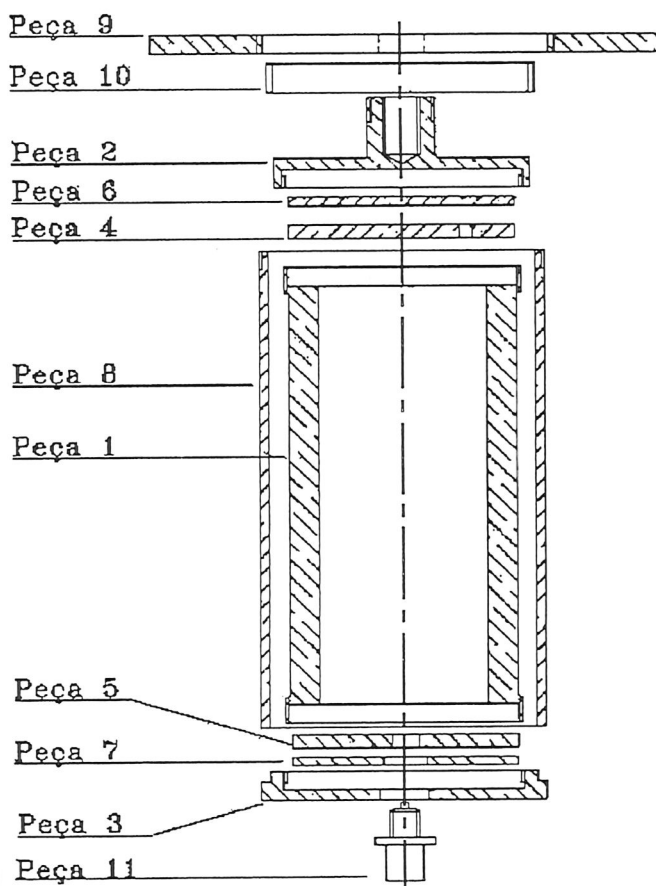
Desenho explodido e em corte das peças do “Shunt” proposto.
